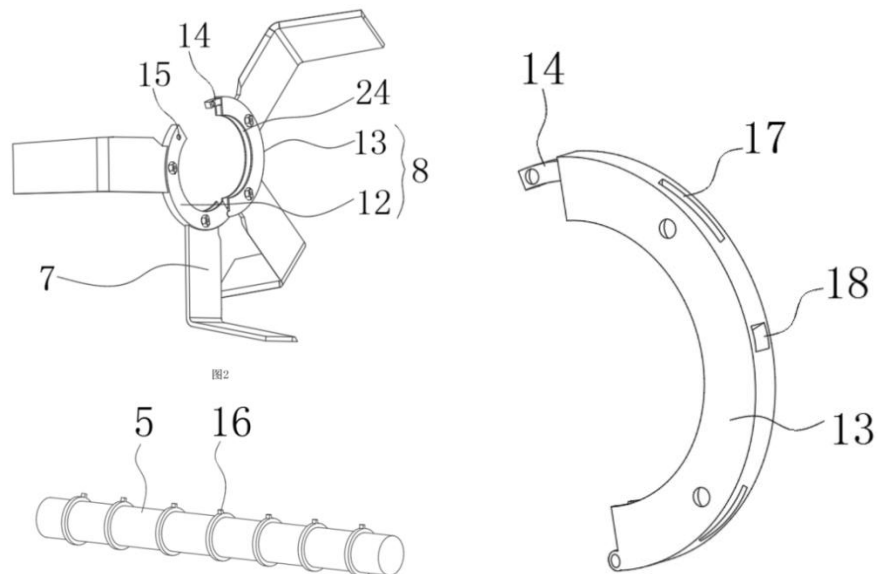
Общий вид фрезы с быстросъемными рабочими органами
